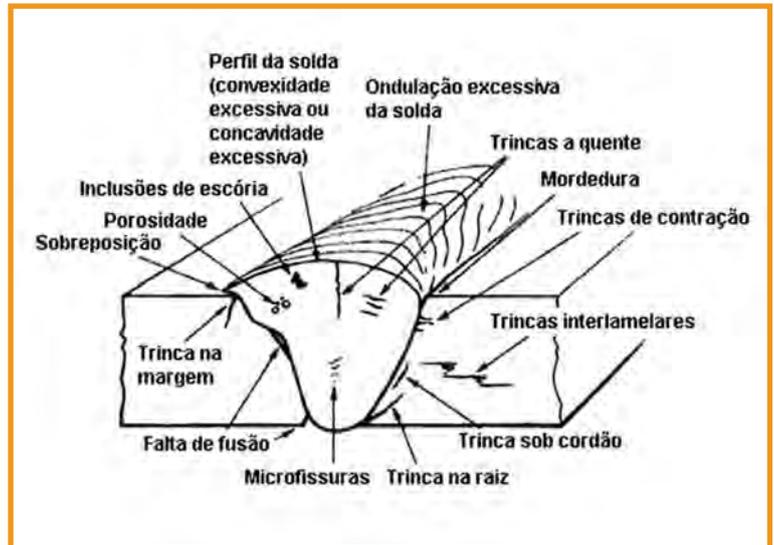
Representação esquemática de defeitos de solda em uma junta de topo com penetração incompleta, que podem resultar em corrosão em frestas das peças quando em serviço ¹
